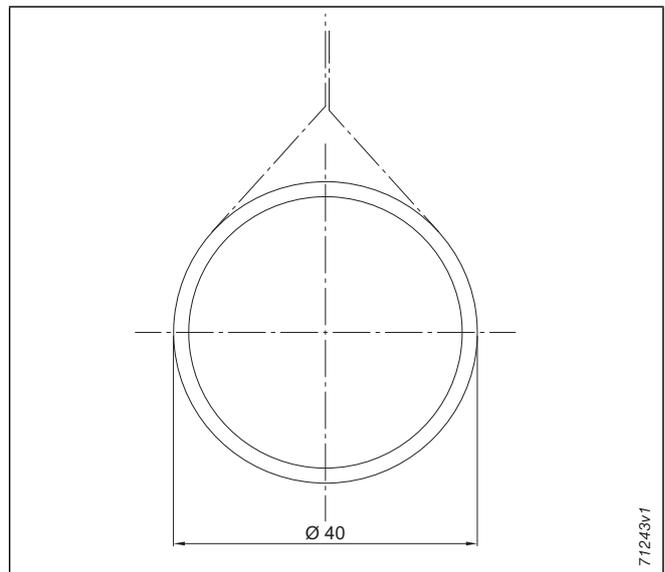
Fallprofil rund, groß, stoffumschlungen
